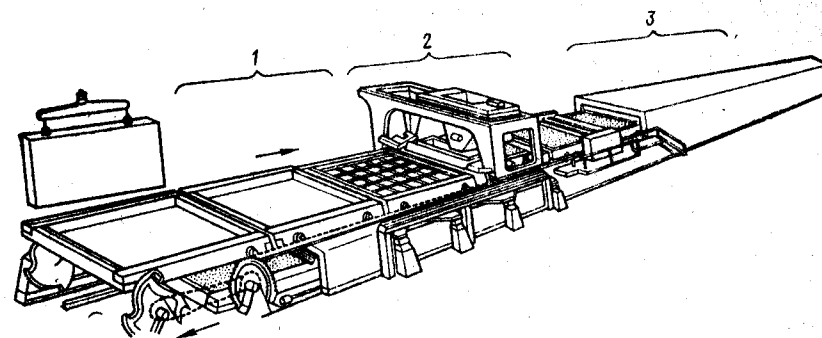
Двухъярусный стан для изготовления сборных железобетонных изделий: 1 — пост подготовки форм и установки арматуры; 2 — пост формования; 3 — камера тепловой обработки
